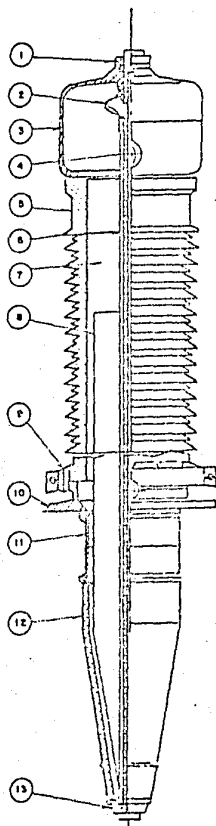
MONTAJE DE UNA BOQUILLA
